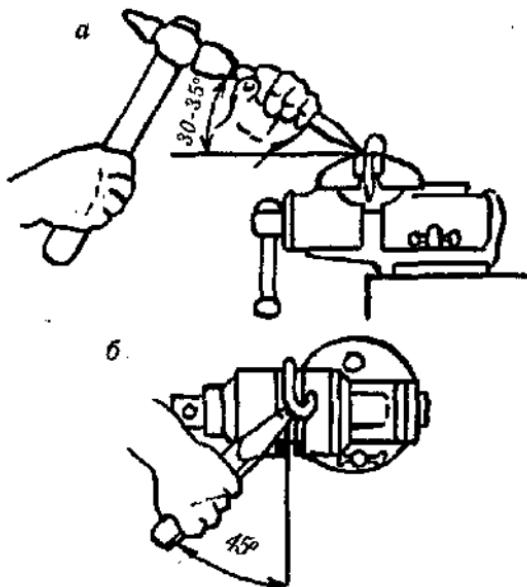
Рубка зубилом: а — вид сбоку; б — вид сверху.
